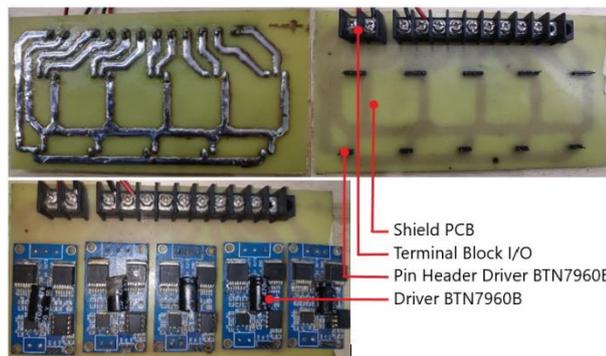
Hasil Desain *Shield* PCB BTN7960B
